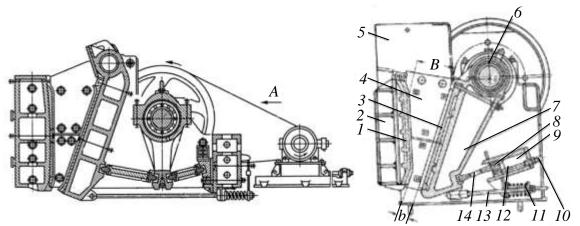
Щековая дробилка со сложным движением щеки: 1 — неподвижная дробящая плита; 2 — передняя стенка; 3, 4 — футеровочные плиты; 5 — защитный кожух; 6 — приводной вал; 7 — подвижная щека; 8 — ползун; 9 — задняя балка; 10 — винт; 11 — пружина; 12 — регулировочное устройство; 13 — тяга; 14 — распорная плита
